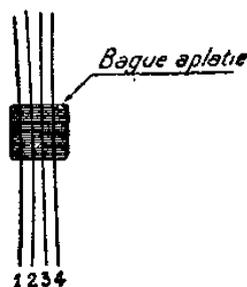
Fils de connexion de la lampe soudés dans la bague.
